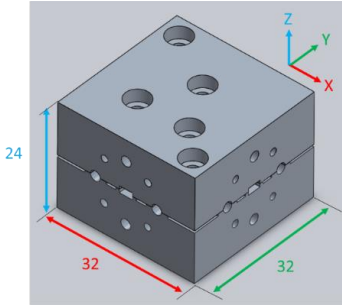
Modèle Solidworks du boîtier du circulateur. Les dimensions sont en millimètres.
